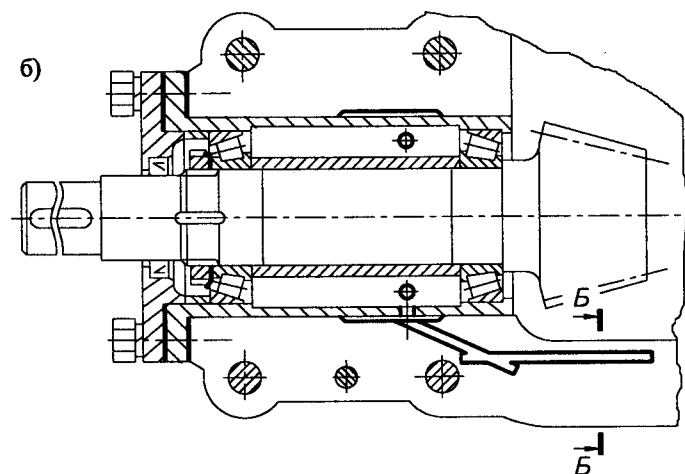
Конструктивные решения по смазыванию подшипников и зубчатых колес редукторов:
